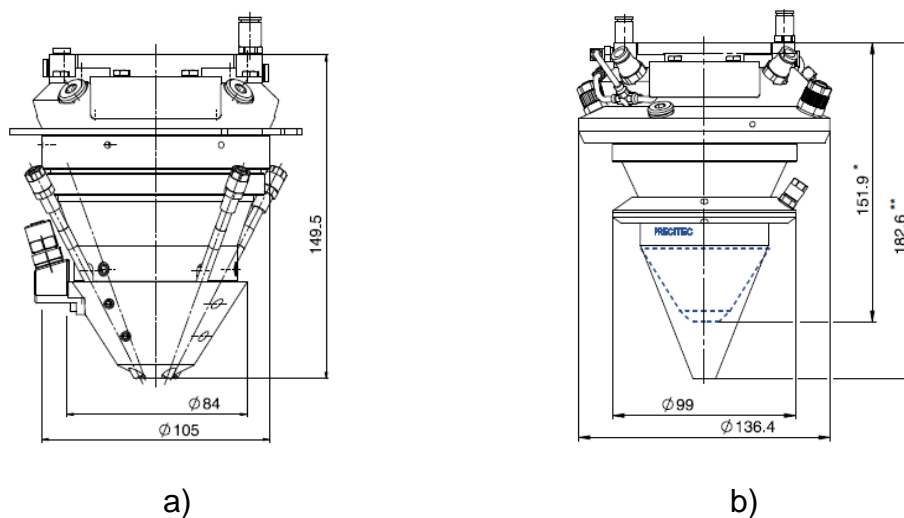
Dimensiones de las boquillas utilizadas: a) Módulo de la boquilla discreta de 4 vías; b) Módulo de la boquilla coaxial continua de 151.9 mm de longitud.
